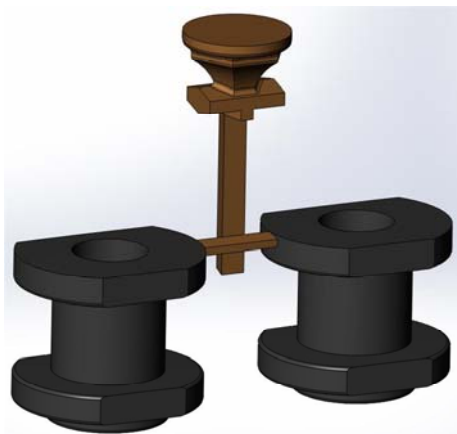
Отливки «Корпус» с литниково-питающей системой
